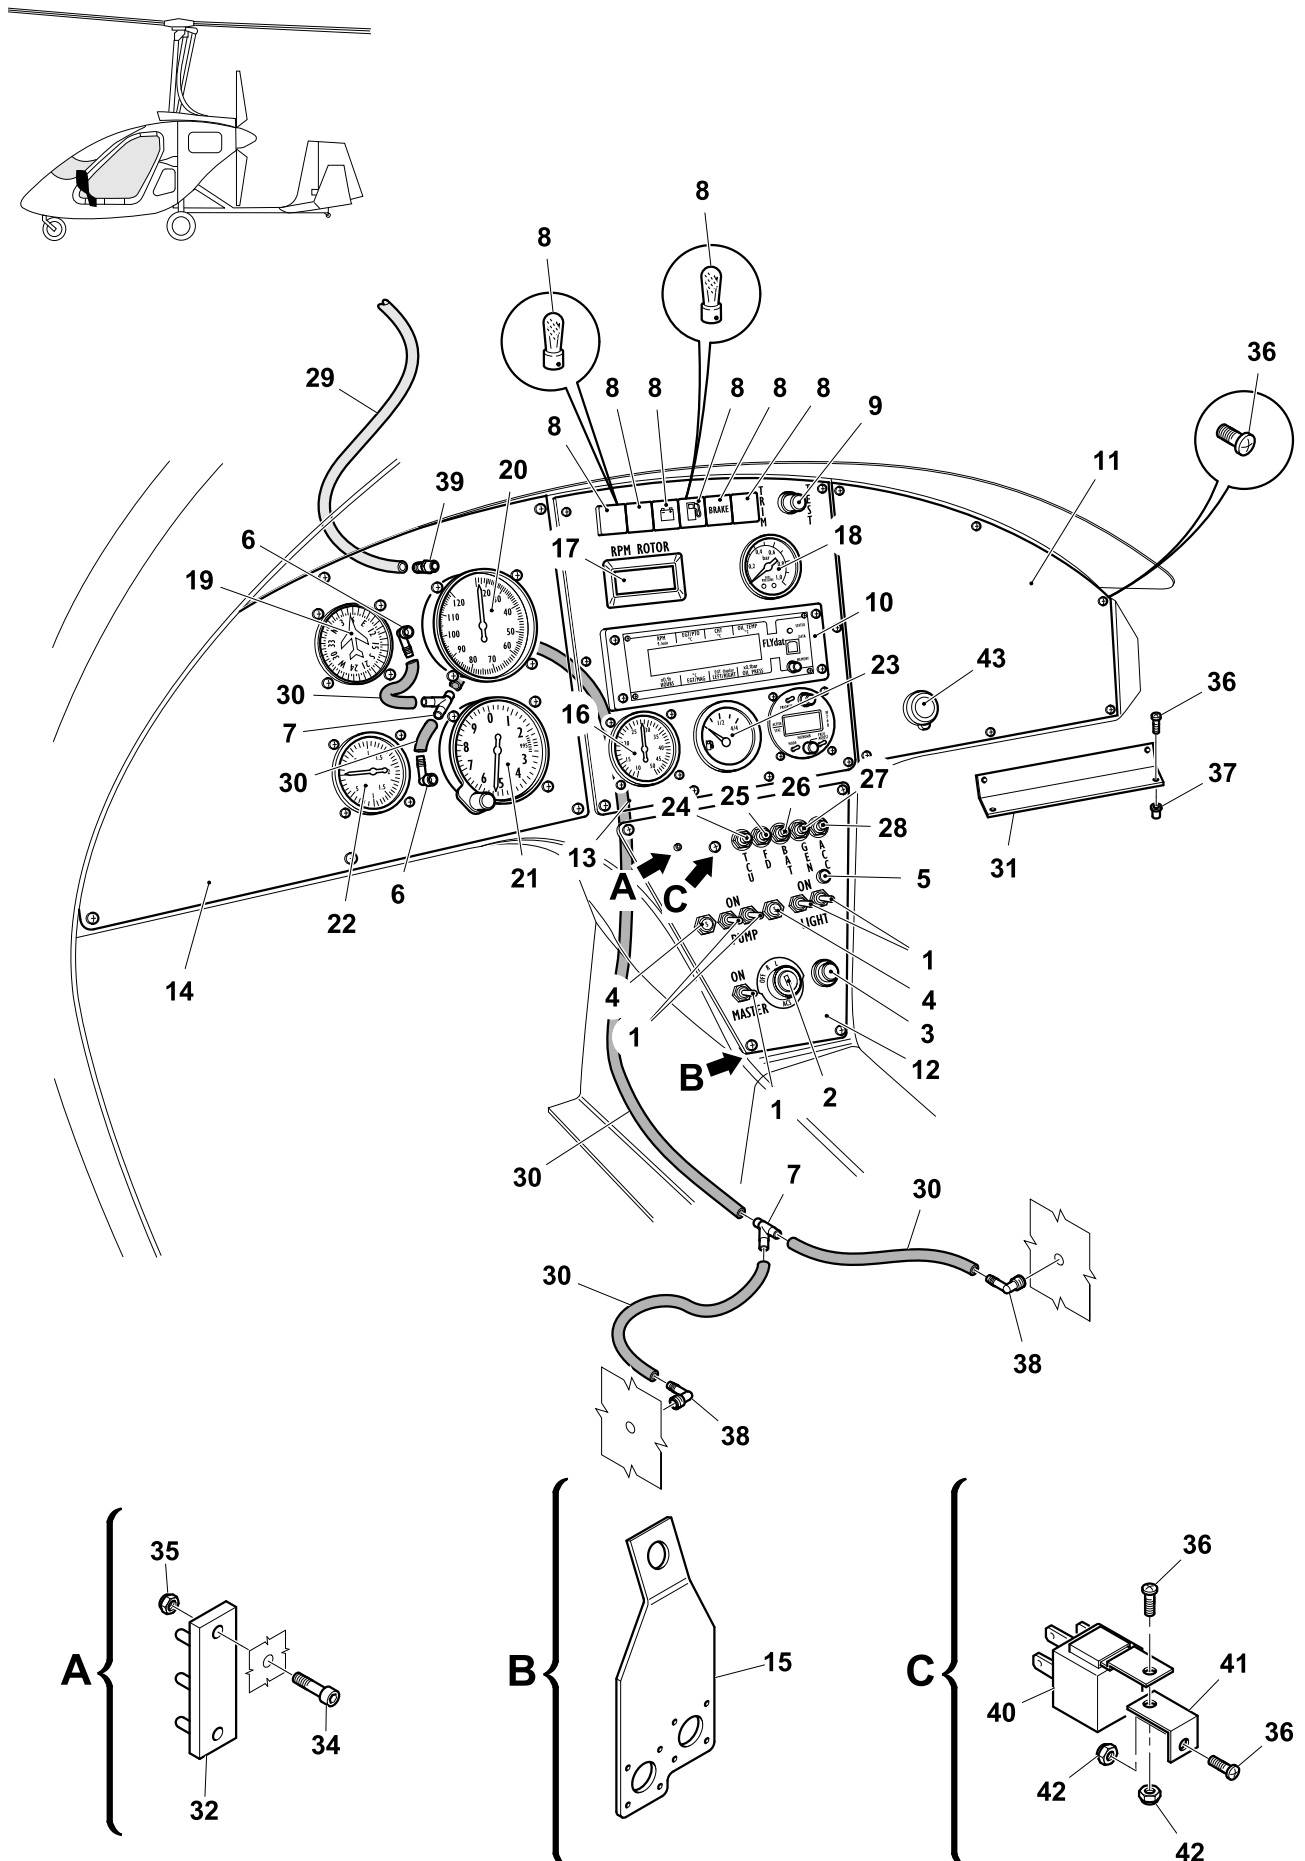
COMPONENTI ELETTRICI 1^a parte
